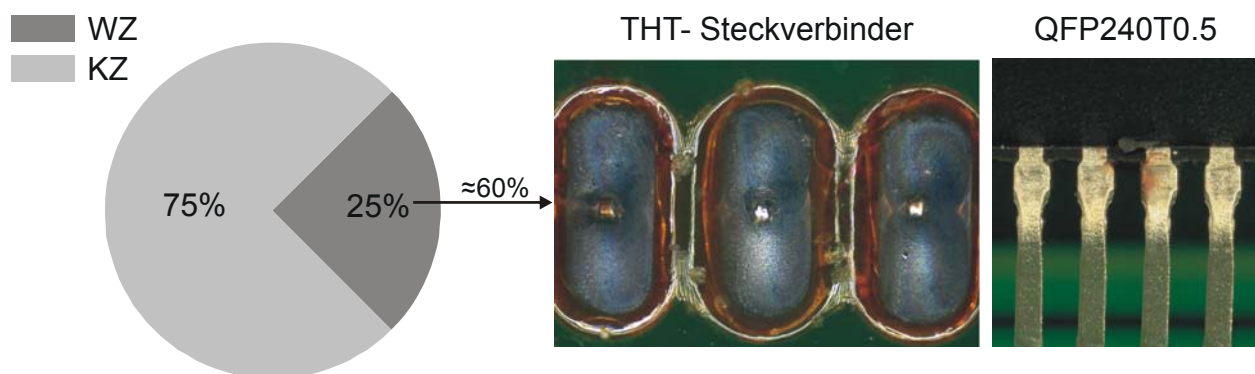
Belastungsabhängige Ausfallverteilung und primär betroffene Bauelemente in den Wärmezyklen
